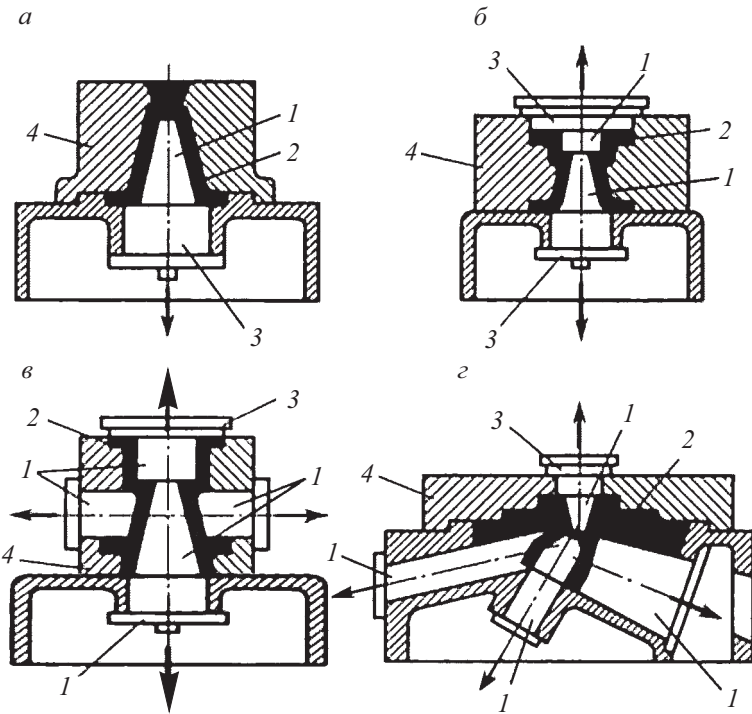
Способы извлечения металлических стержней из полости отливки: а, б – параллельно размыканию кокиля; в, г – под разными углами к направлению размыкания кокиля; 1 – металлический стержень; 2 – отливка; 3 – хвостовик стержня; 4 – половинка или целый кокиль
